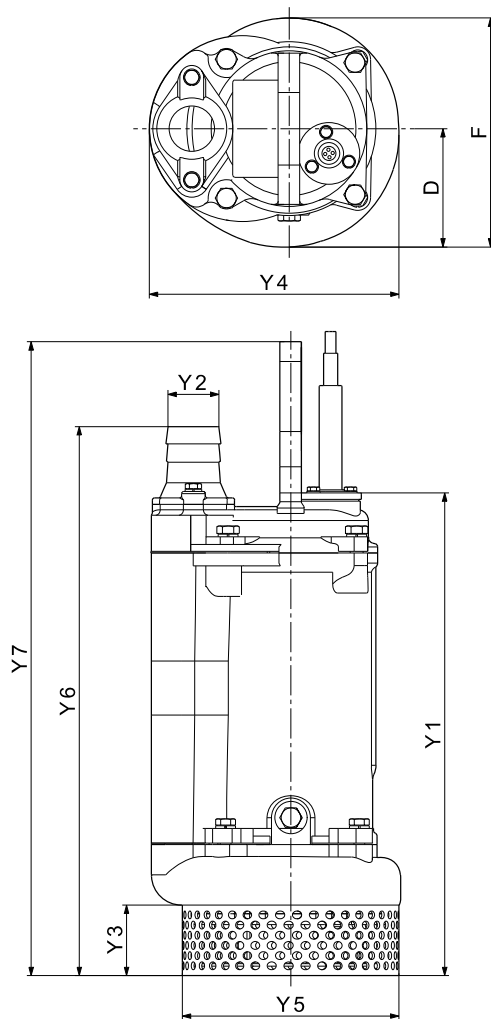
Размеры насоса DWK.O с соединением для шланга
